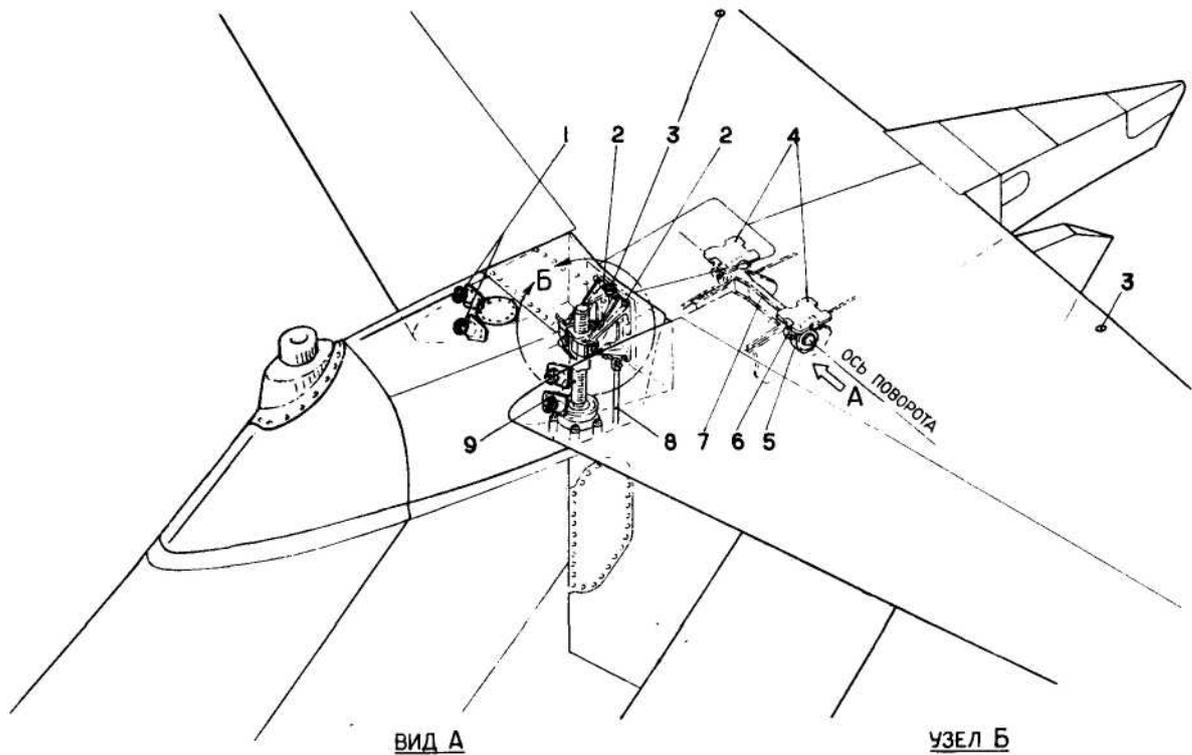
СТЫКОВКА СТАБИЛИЗАТОРА С КИЛЕМ
